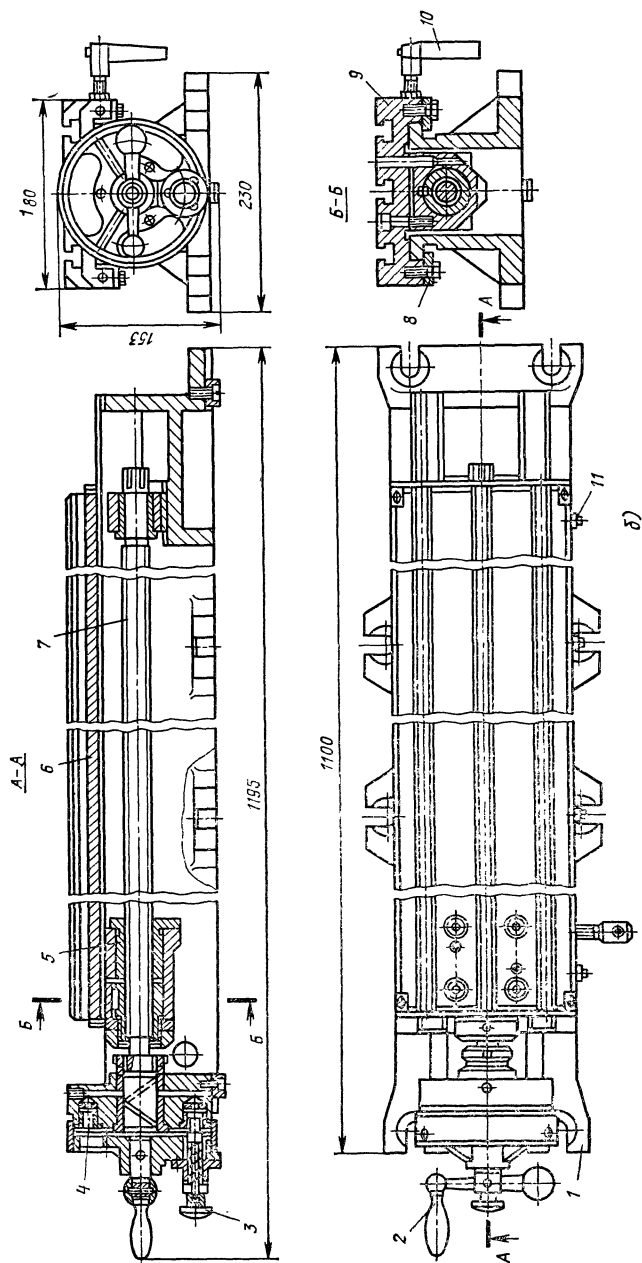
Специализированные безаладожные приспособления для фрезерования:
